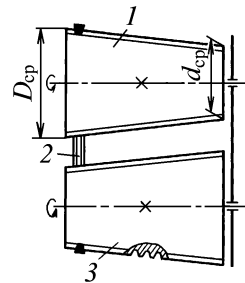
Схема приспособления для нарезания резьбы с неравномерным шагом:
